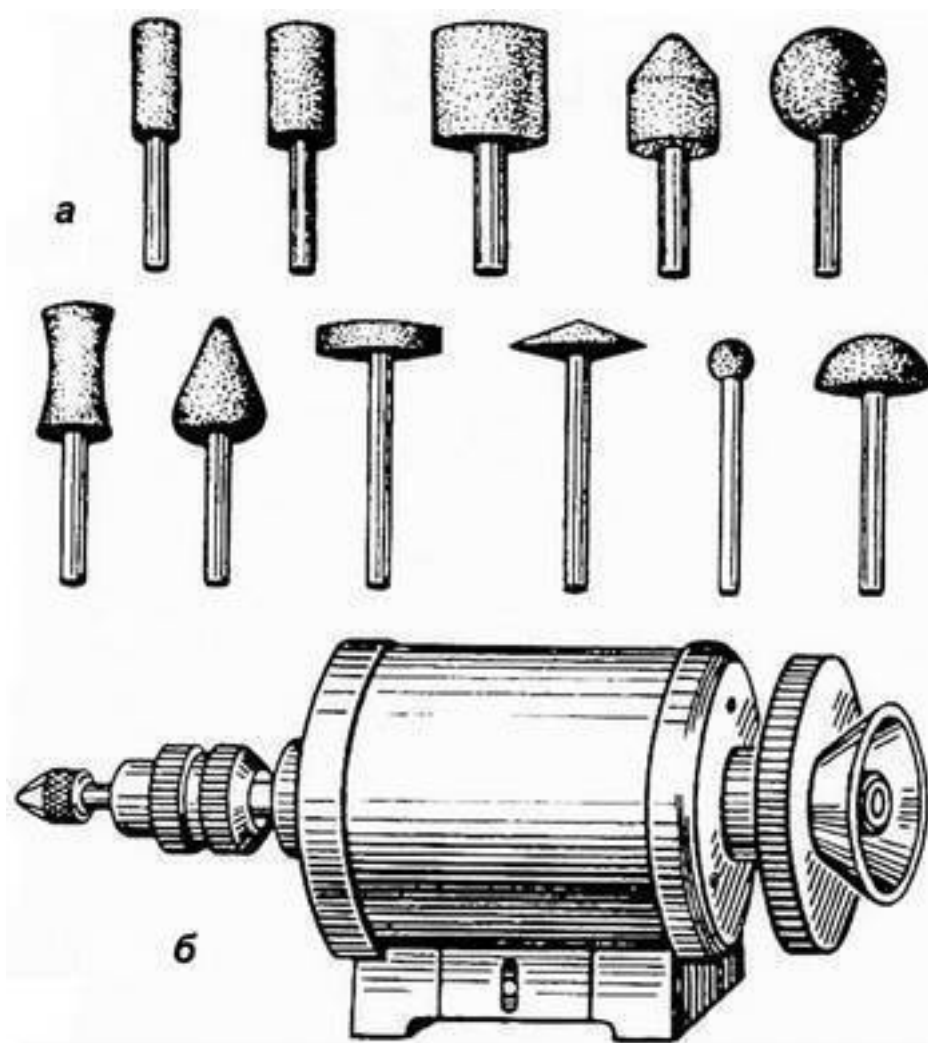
Заточный инструмент: а – абразивные головки; б – двигатель с насадками
